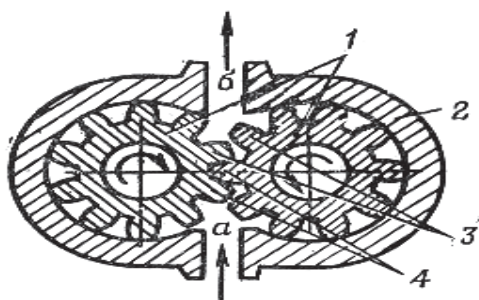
Схема шестеренного насоса: а – полость всасывания; б – полость нагнетания; 1 – шестерни; 2 – корпус; 3, 4 – зубья шестерен
